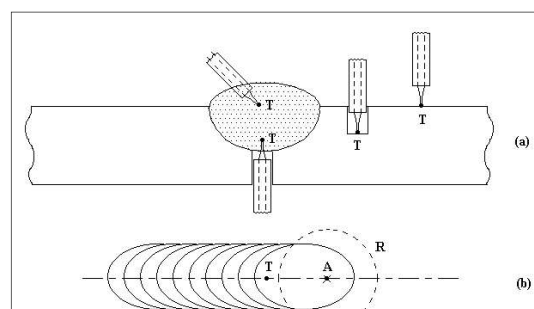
(a) Diversas posições de termopares (T) na junta soldada; (b) O termopar (T) deve “arpoar” a poça de fusão numa região que não está sob direta ação do arco elétrico (R).
